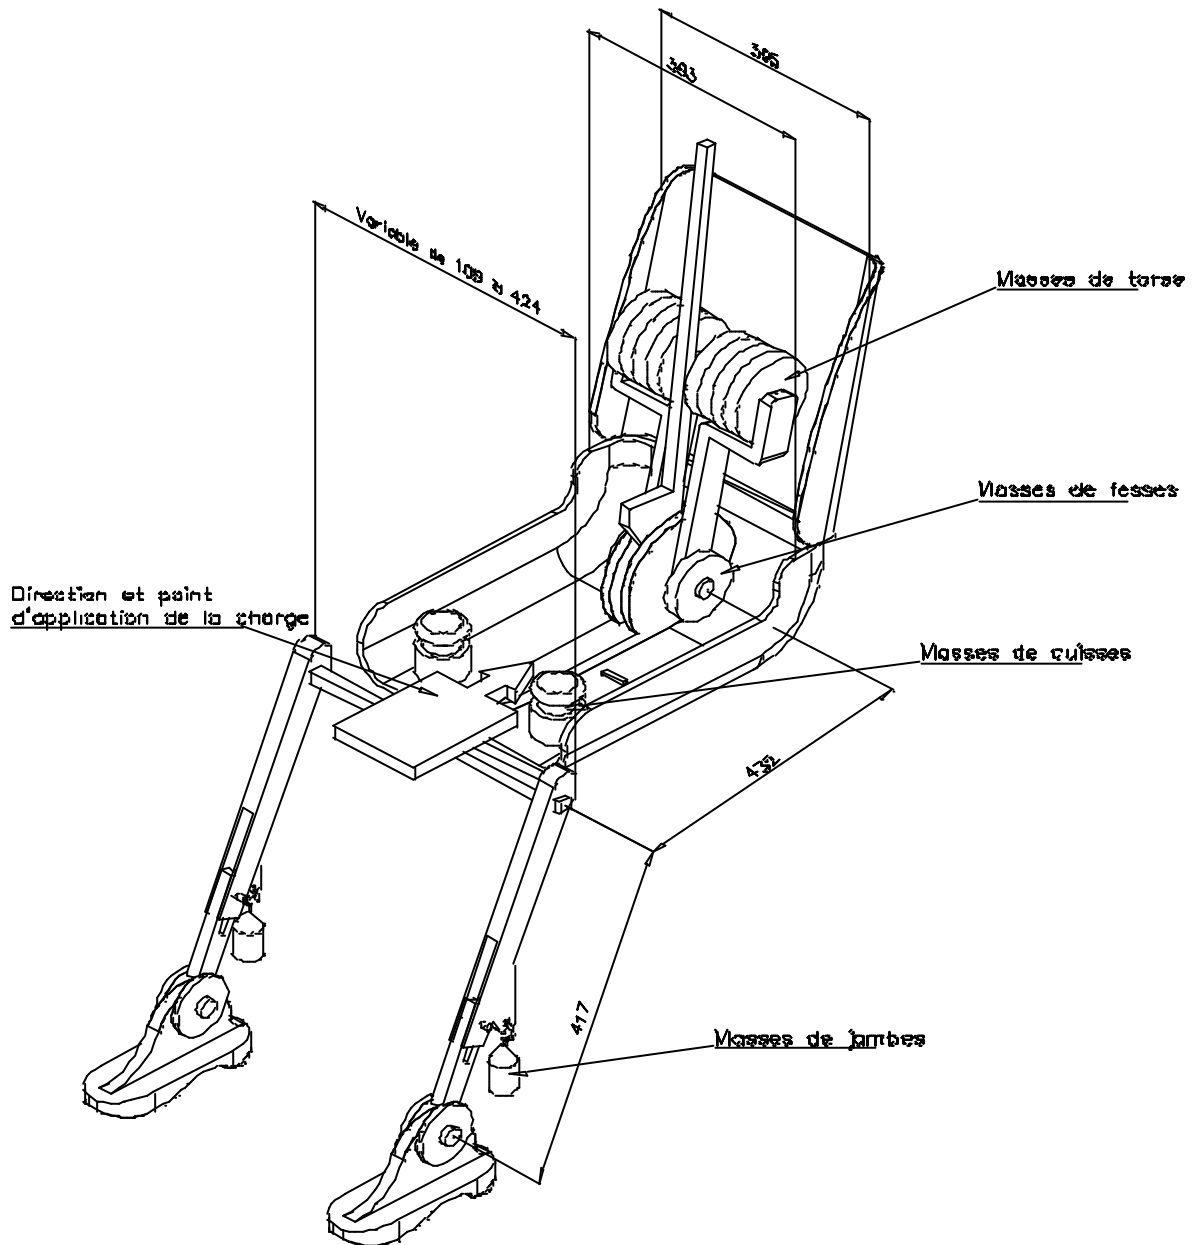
Dimensions des éléments de la machine 3-D H et emplacement des masses
